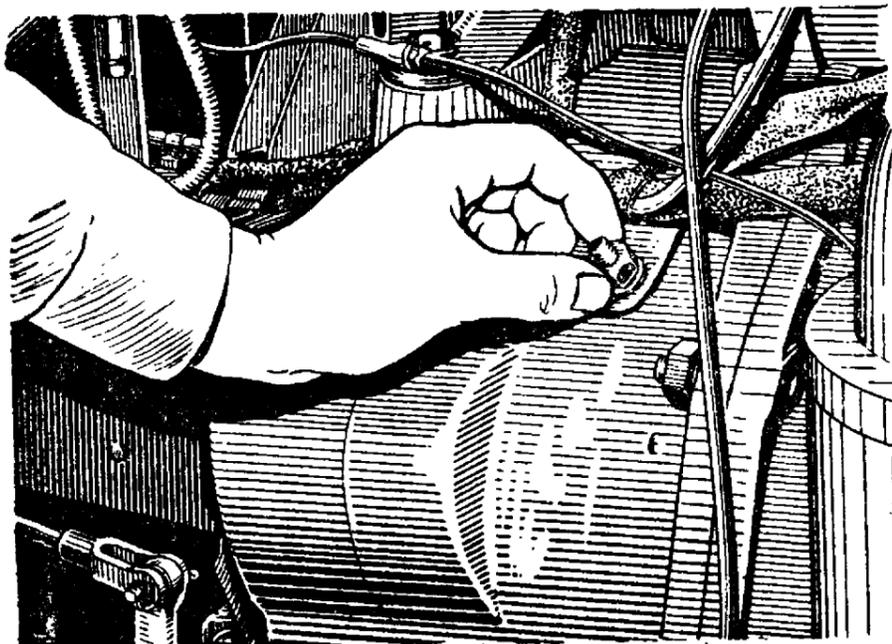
Установка шпильки гладким концом в соединительный корпус.
